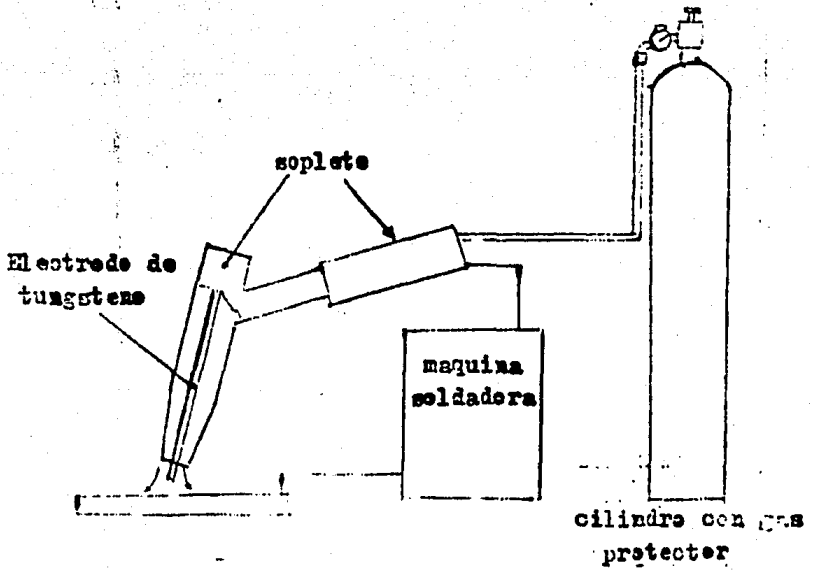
Diagrama esquemático del equipo empleado para la soldadura con el proceso TIG.
